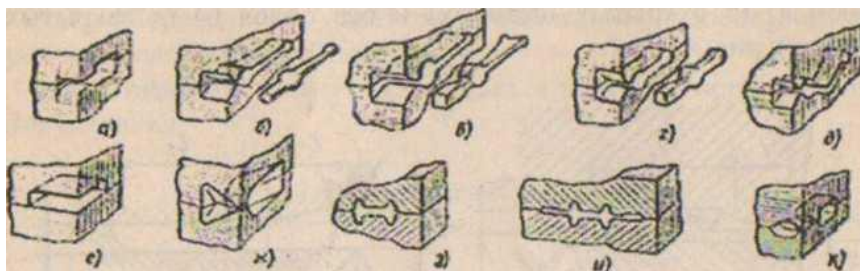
Ручьи молотовых штампов: а, к - протяжной; б - подкатной; в - пережимной; г - формовочный; д - гибочный; е - осадочный; ж - отрубной; з - предварительный (черновой); и - чистовой.
